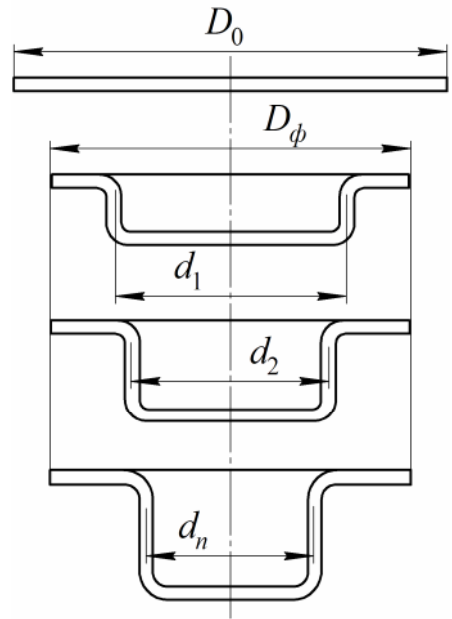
Схема переходів витяжки деталей із широким фланцем
